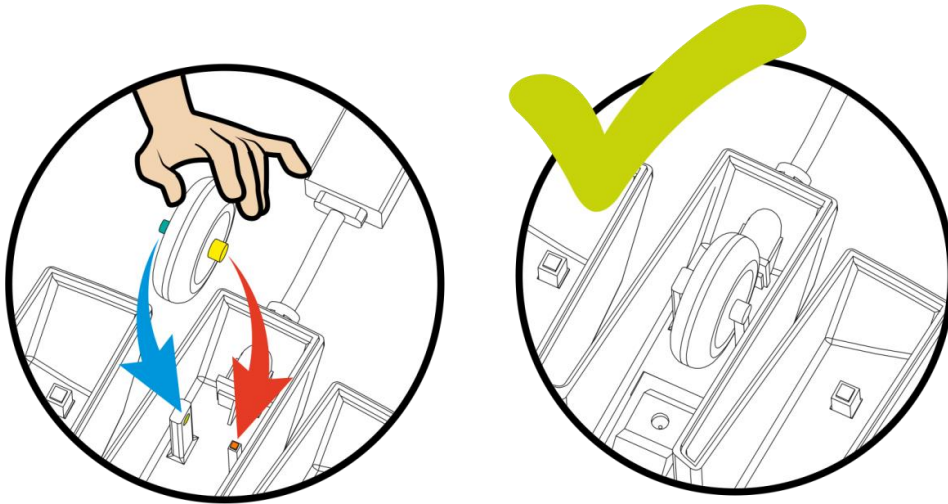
Ensamblaje 1.1 – 1.4
